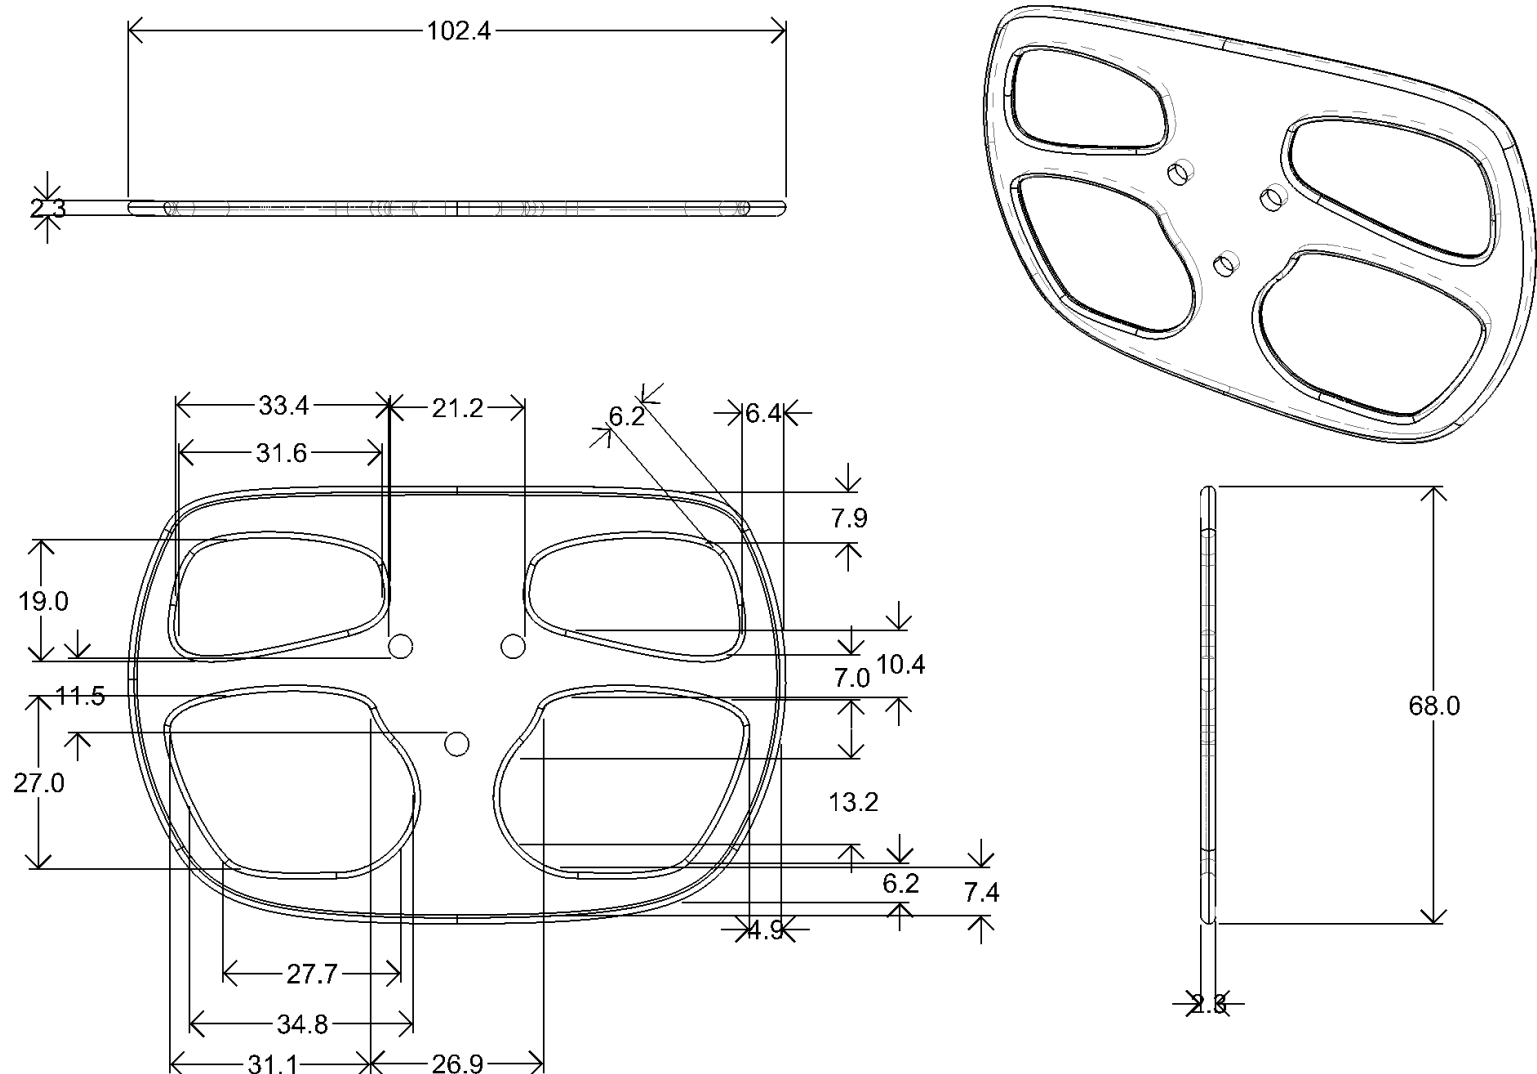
Plano de la placa base del volante (proporcionado por el equipo)
